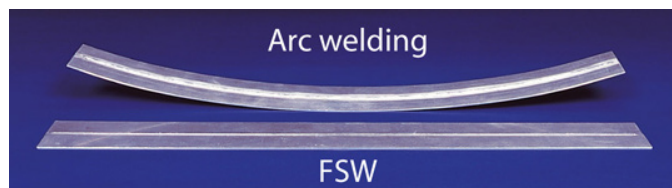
Distorsions induites par le soudage à l'arc et par le FSW [175].
